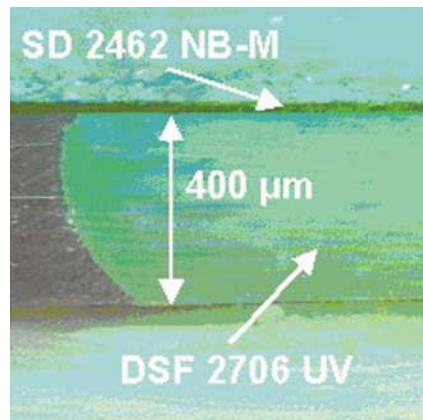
Schliffbild einer 400 µm-Leiterplatte
